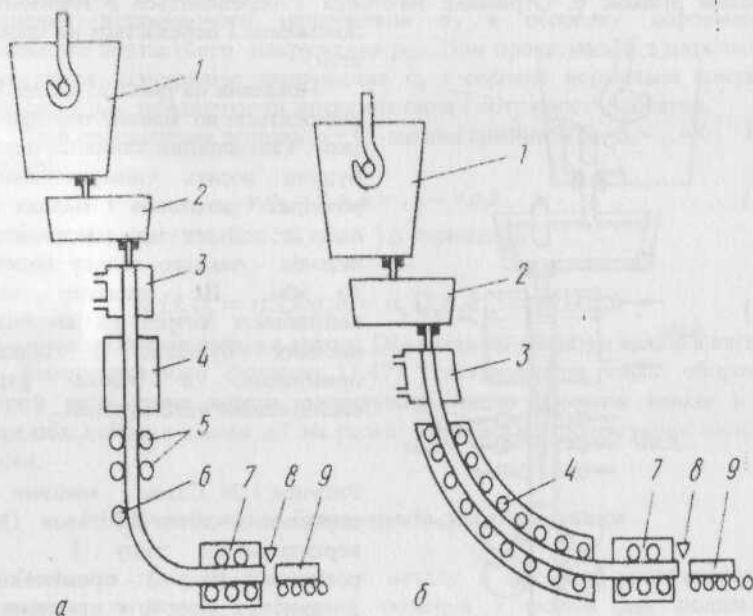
Схеми МНЛЗ вертикального типу з вигином заготовки (а) і радіального типу (б) : 1 - сталерозливний ківш; 2 - проміжний ківш; 3 - кристалізатор; 4 - вторинна зона охолодження; 5 - ролики, що тягнуть; 6 - пристрій для вигину заготовки; 7 - правильна машина; 8 - пристрій для різання заготовки; 9 - заготовка
